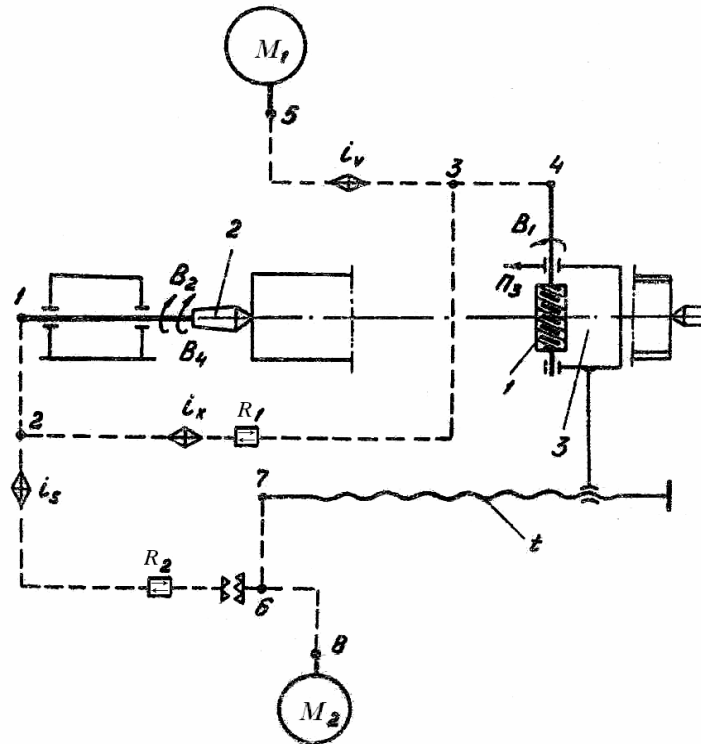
Типовая кинематическая структура шлицефрезерного станка
